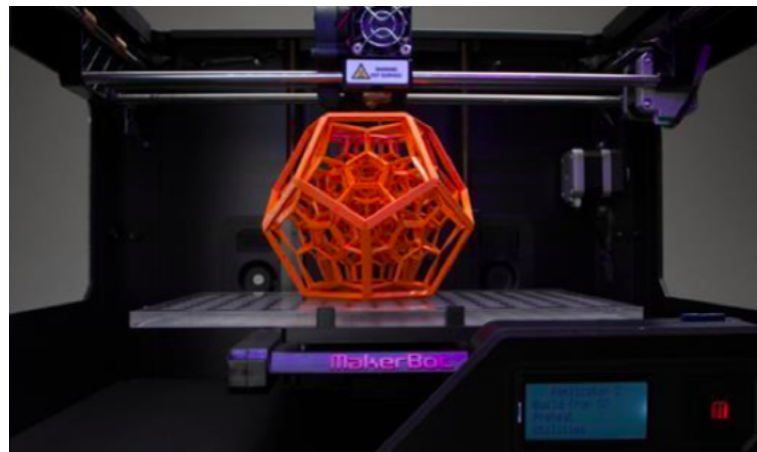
Pieza obtenida mediante proceso de extrusión de material [18].
